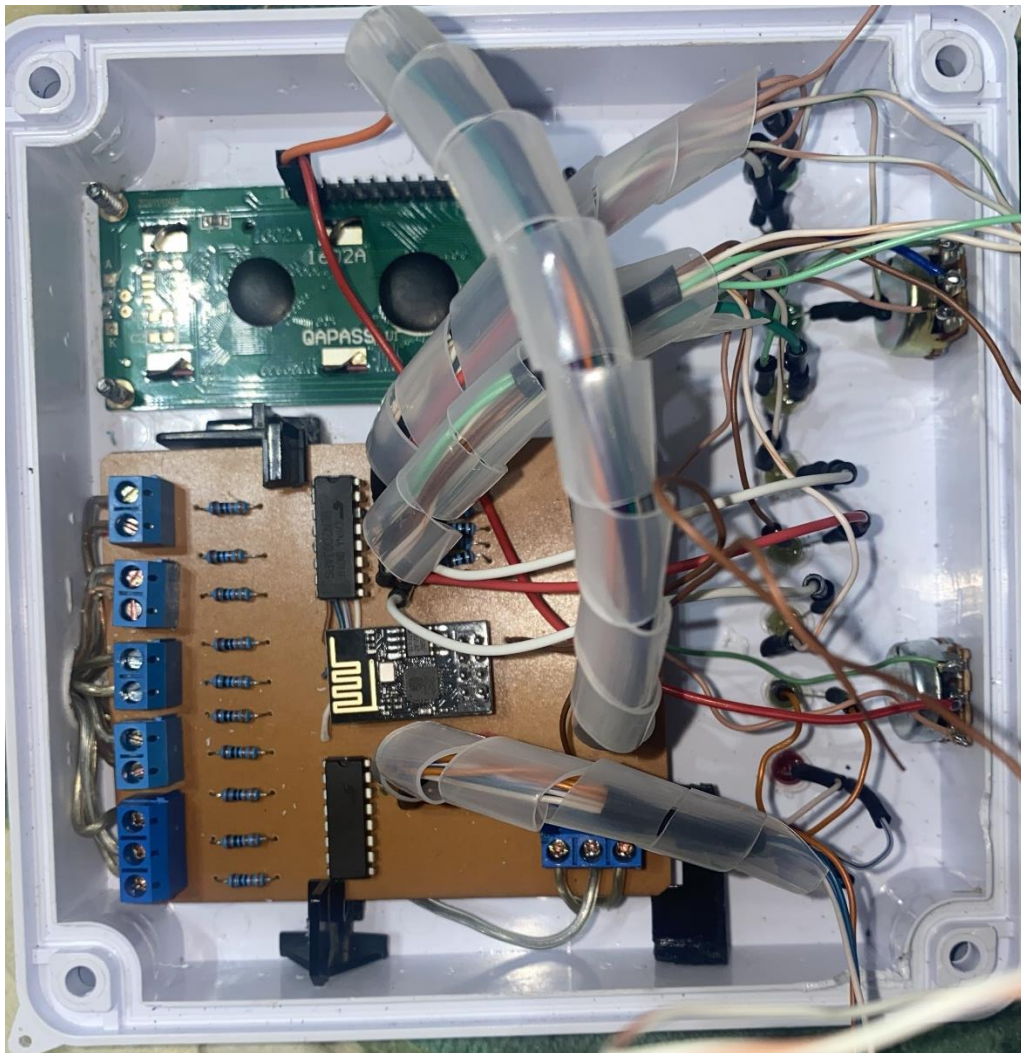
Placa de circuito impreso (PCB) en Físico
